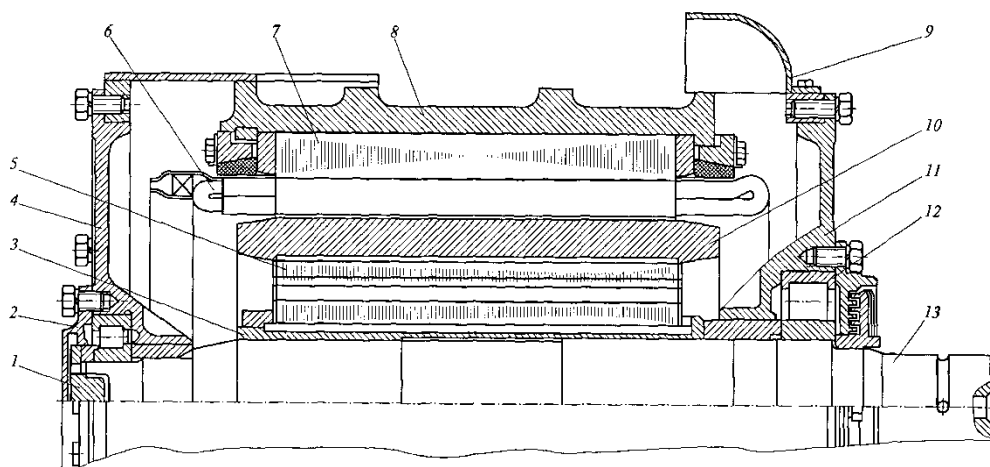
Асинхронный тяговый двигатель ЭД900.
